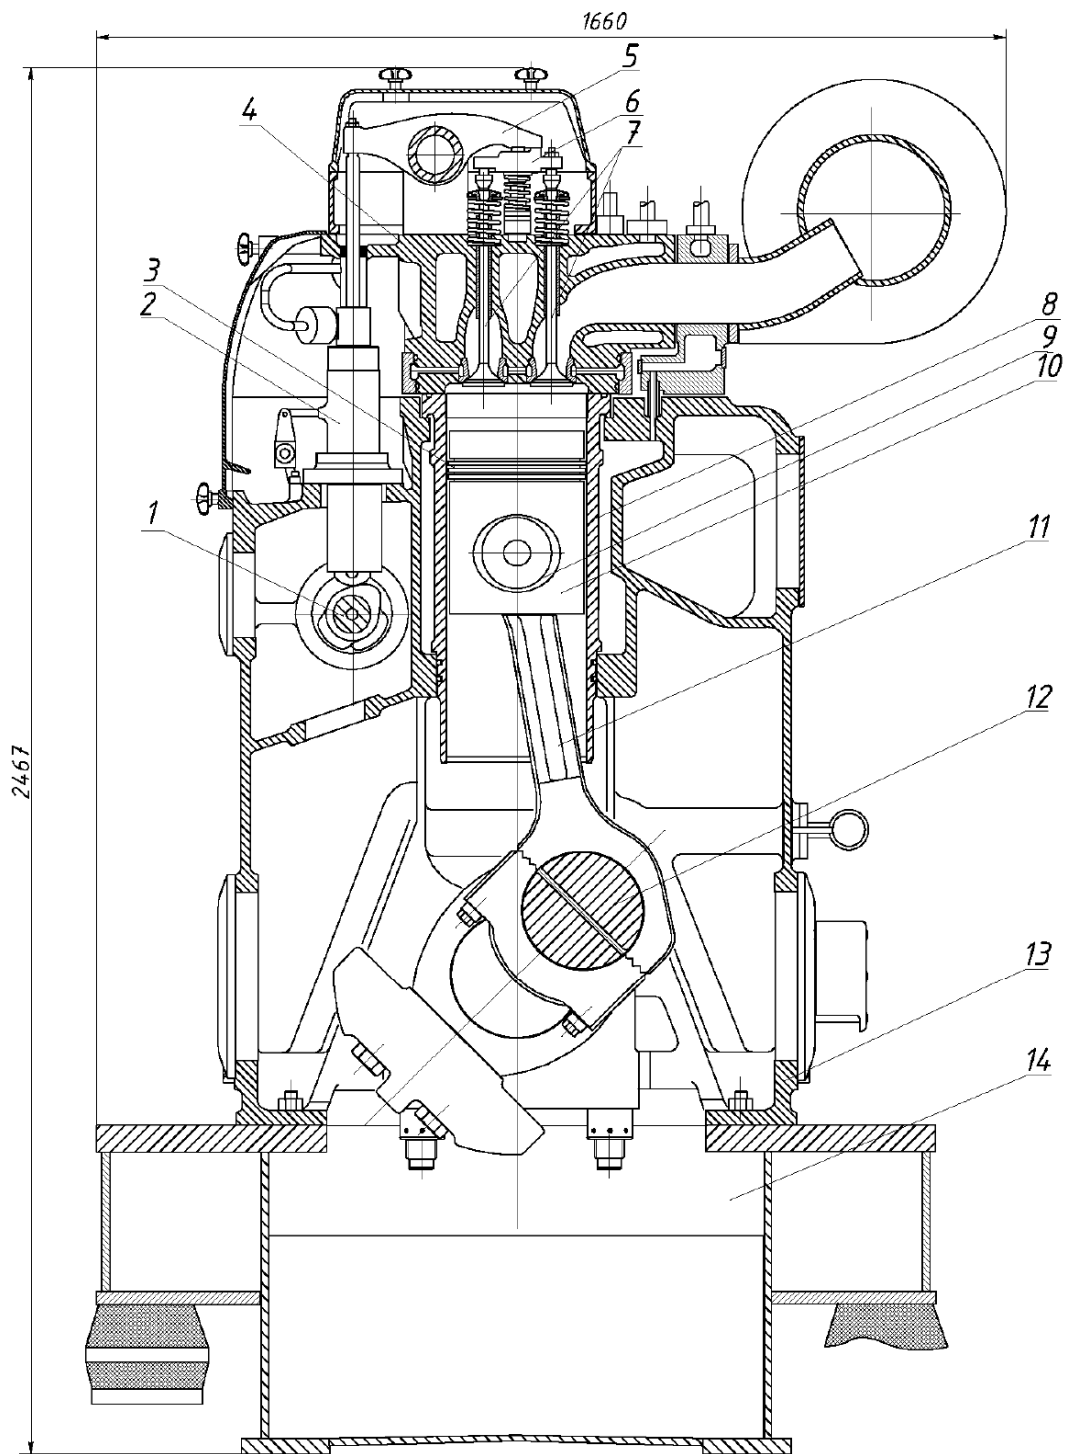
Загальне компонування суднового чотиритактного високооборотно-го двигуна 6CH23/30: 1 – розподільний вал привода клапанів та ПНВТ; 2 – ПНВТ; 3 – поршневі кільця; 4 – кришка циліндра; 5 – коромисло; 6 – штанга штовхача випускного клапана; 7 – випускний клапан; 8 – гільза циліндра; 9 – поршковий палець; 10 – поршень; 11 – шатун; 12 – колінчатий вал; 13 – картер; 14 – кришка картера
